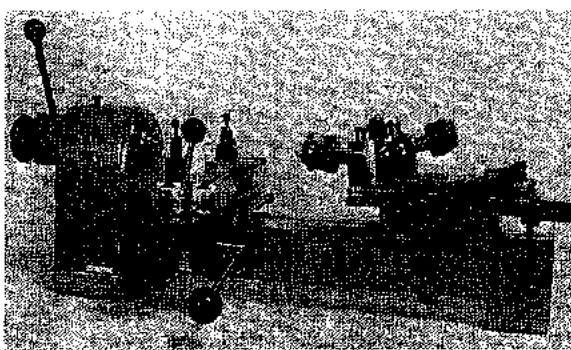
Pequeño torno del tipo de sobre banco (F. W. Derbyshire Inc.)
